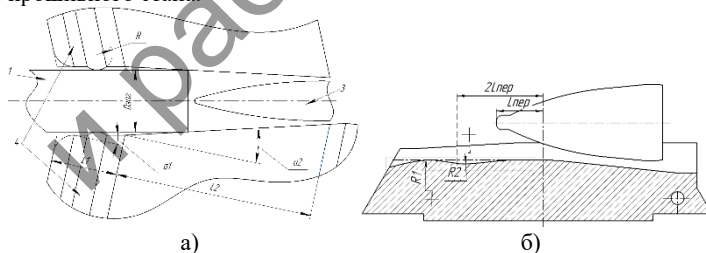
Измененный профиль вала и линейки прошивного стана:
